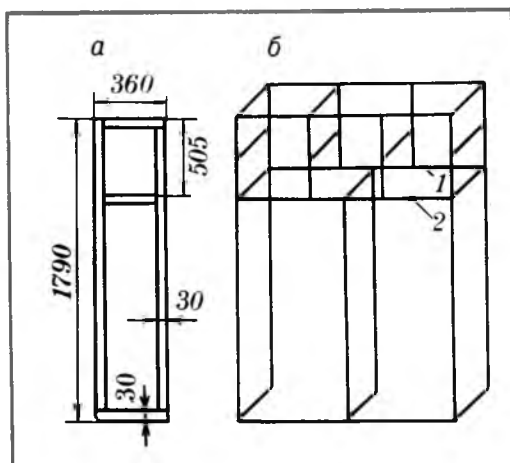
Каркас: а — боковая часть; б — схема; 1—2 — элементы конструкции, к которым крепятся подвесы
